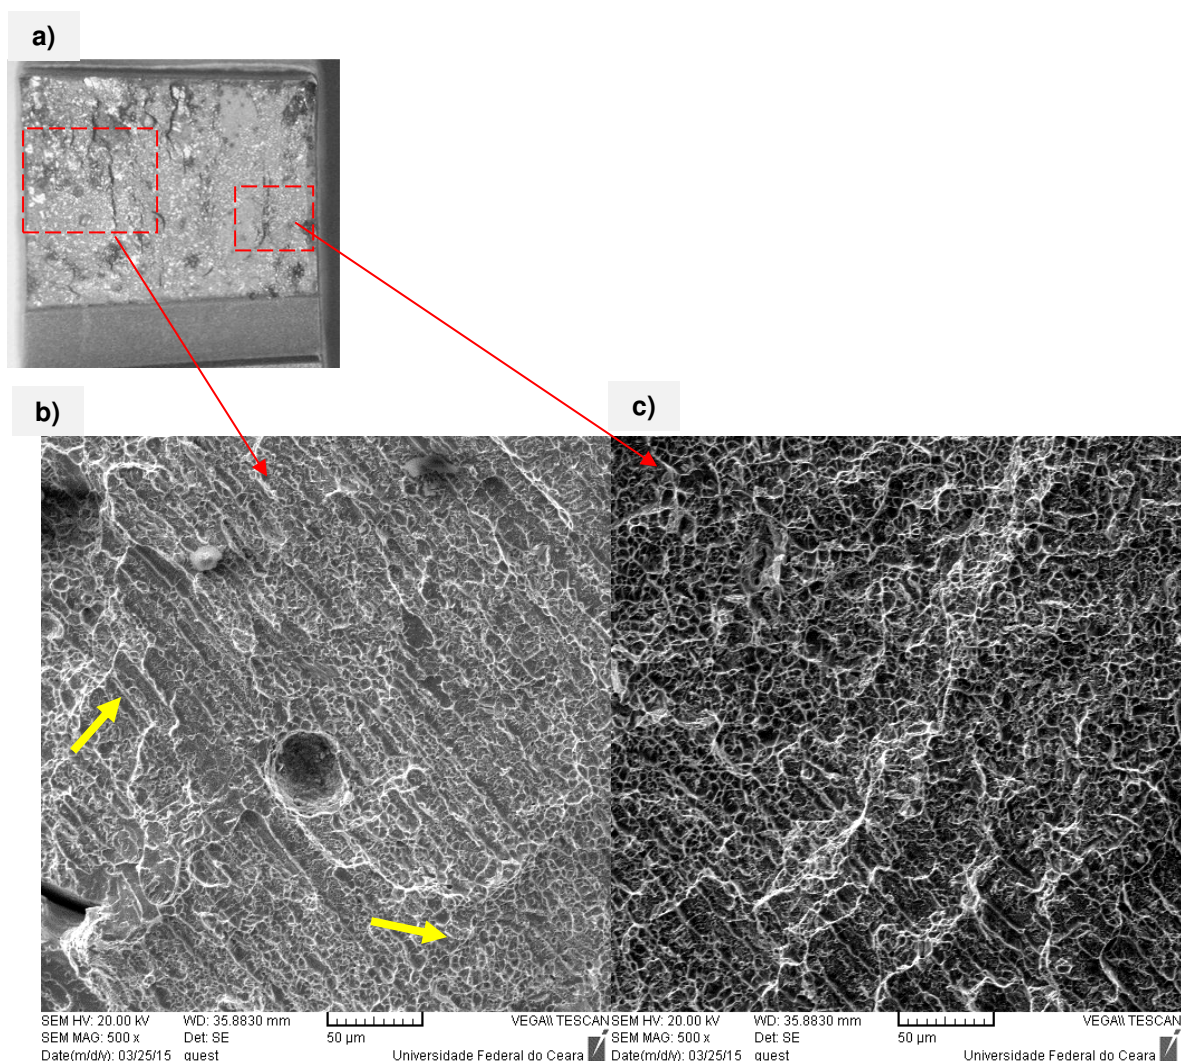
Microscopia eletrônica de varredura (MEV). Superfície de fratura após ensaio de impacto de Charpy. Amostra com entalhe na região do metal base de aço AISI 8530M na junta soldada com *Maraging* 250 – 500X.
